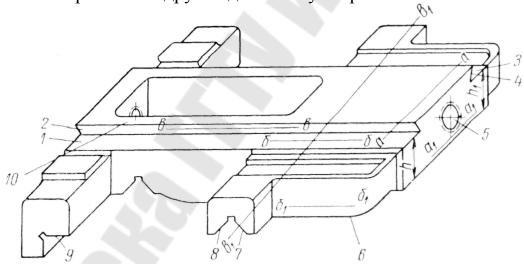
Каретка суппорта токарно-винторезного станка модели 1К62
